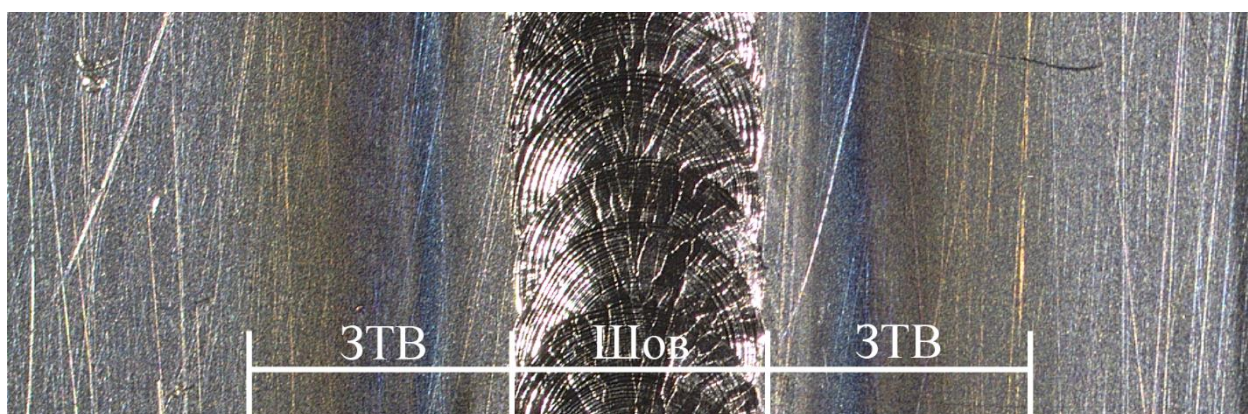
Пример размера сварного шва и ЗТВ
